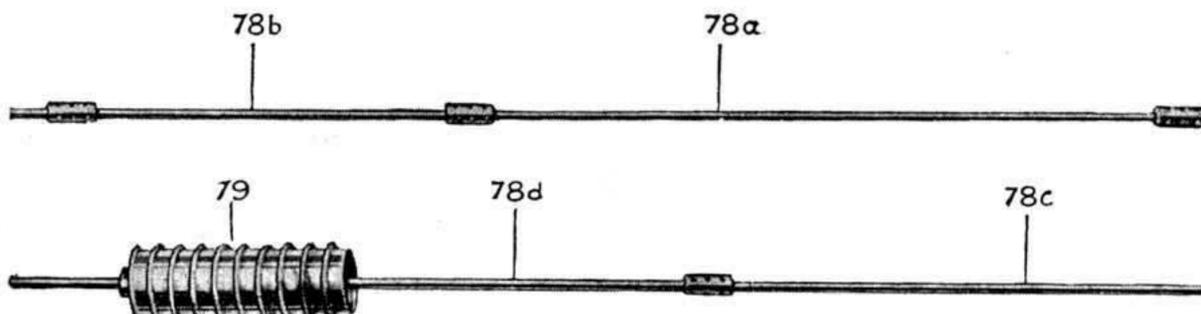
Le Balancier (coupé en deux, vu le manque d'emplacement).
